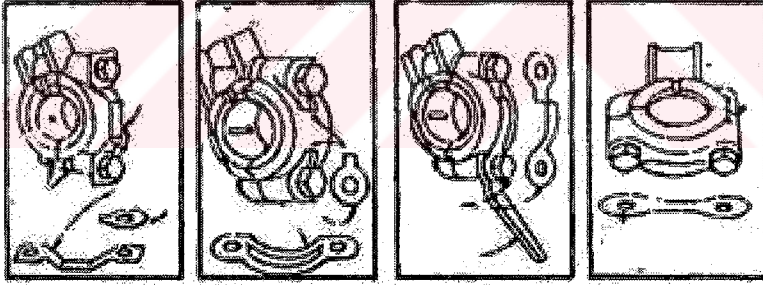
Yağ pompası montaj örneği (Miller & Miller, 1993)
